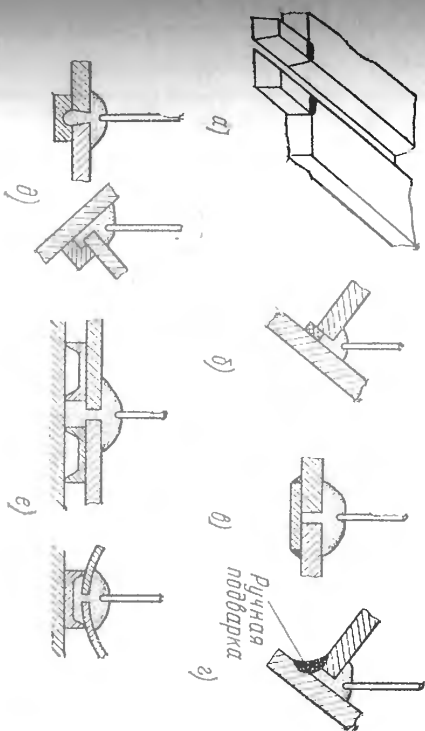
Подготовка заготовок к сварке под флюсом с использованием начальных и выходных планок (а), асбестовой набивки (б), остающейся стальной подкладки (в), предварительной ручной подварки (г), флюсомедной подкладки (д), флюсовой подкладки (е)
